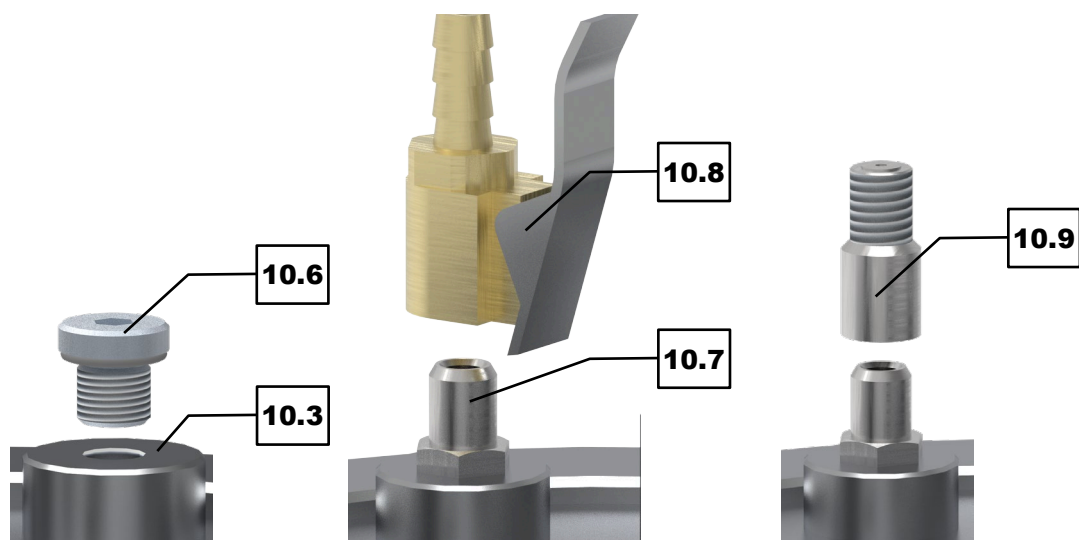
Blindstopfen entfernen (links), Ventil einsetzen und Schlauch anschließen (mitte), Adapter aufsetzen (rechts)
